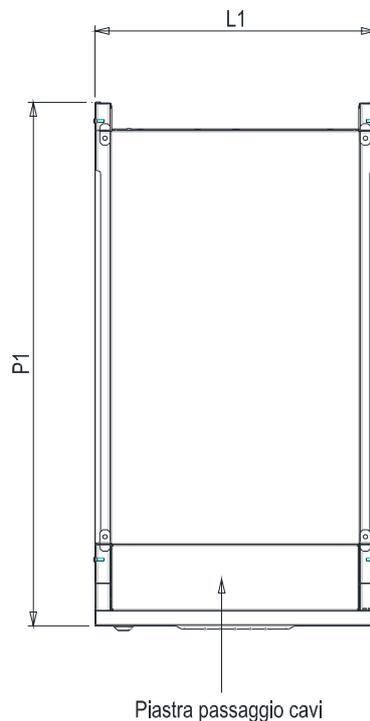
Pianta di base UPS INGENIO 30-40-50kVA
